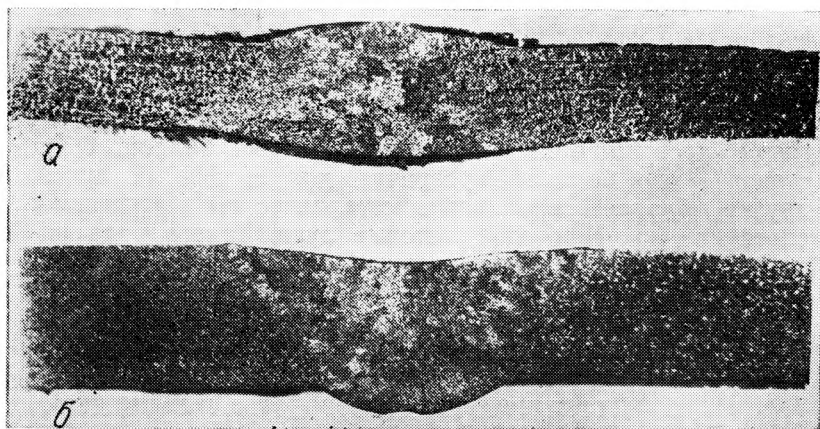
Внешний вид и разрезы образцов из стали X18H10T (а) и сплава ВТ-1 (б), сваренных солнечной энергией.
